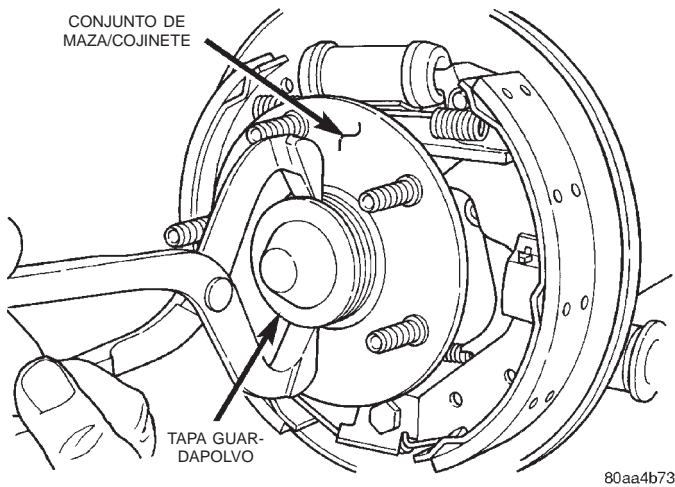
Tapa guardapolvo del conjunto de maza/cojinete trasero
